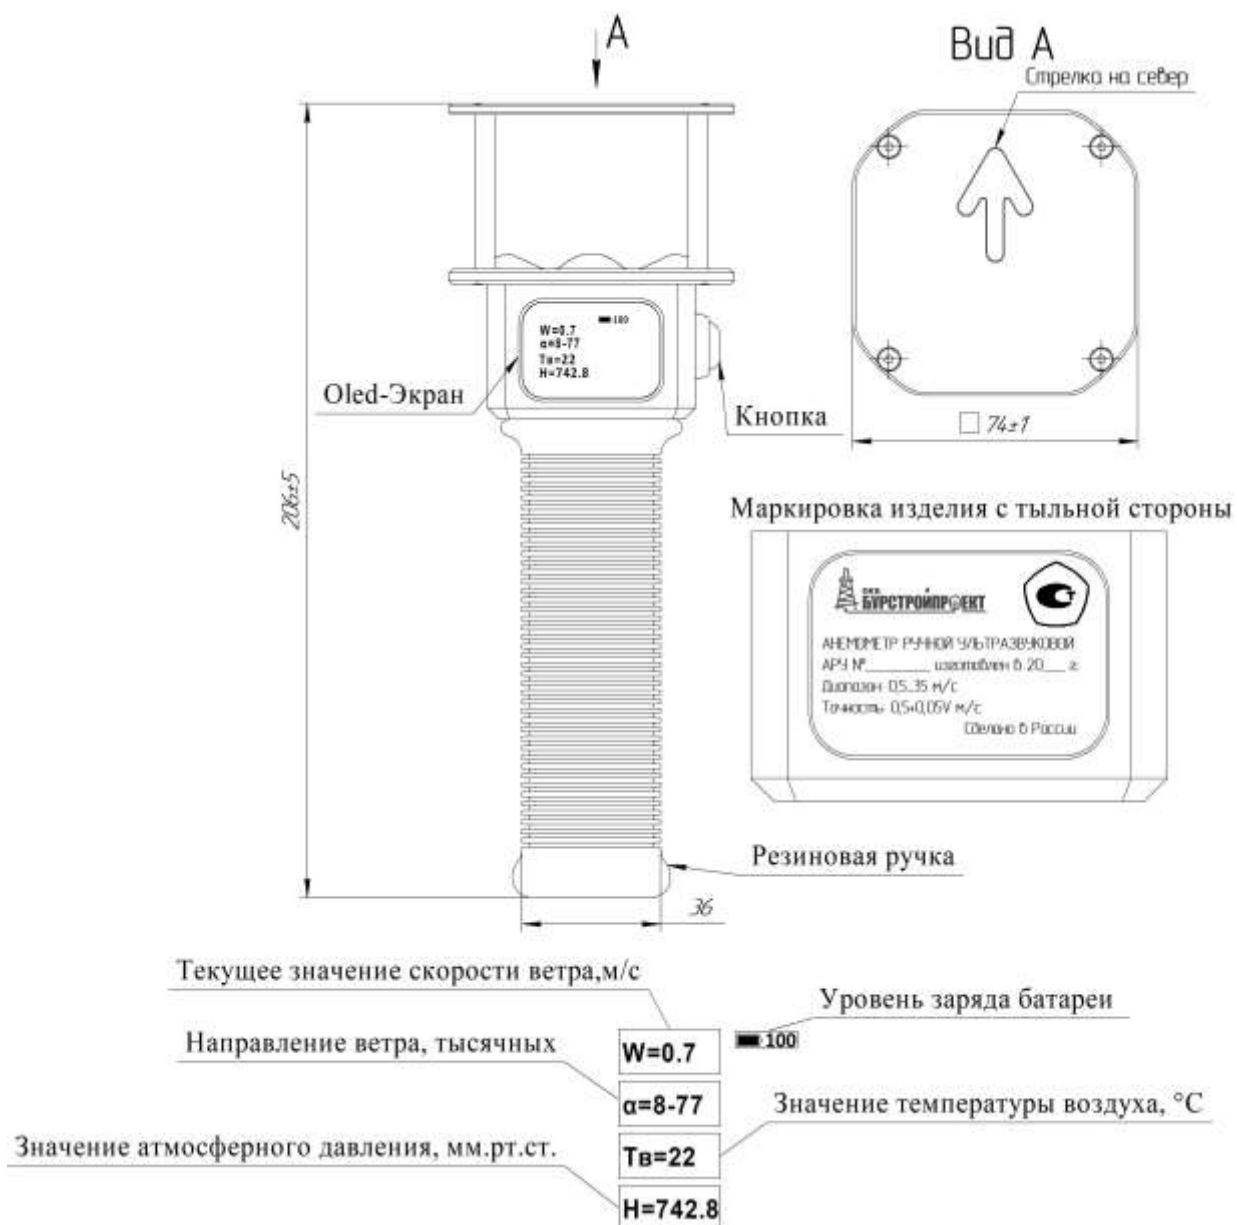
а Внешний вид и габаритные размеры изделия АРУ-А
